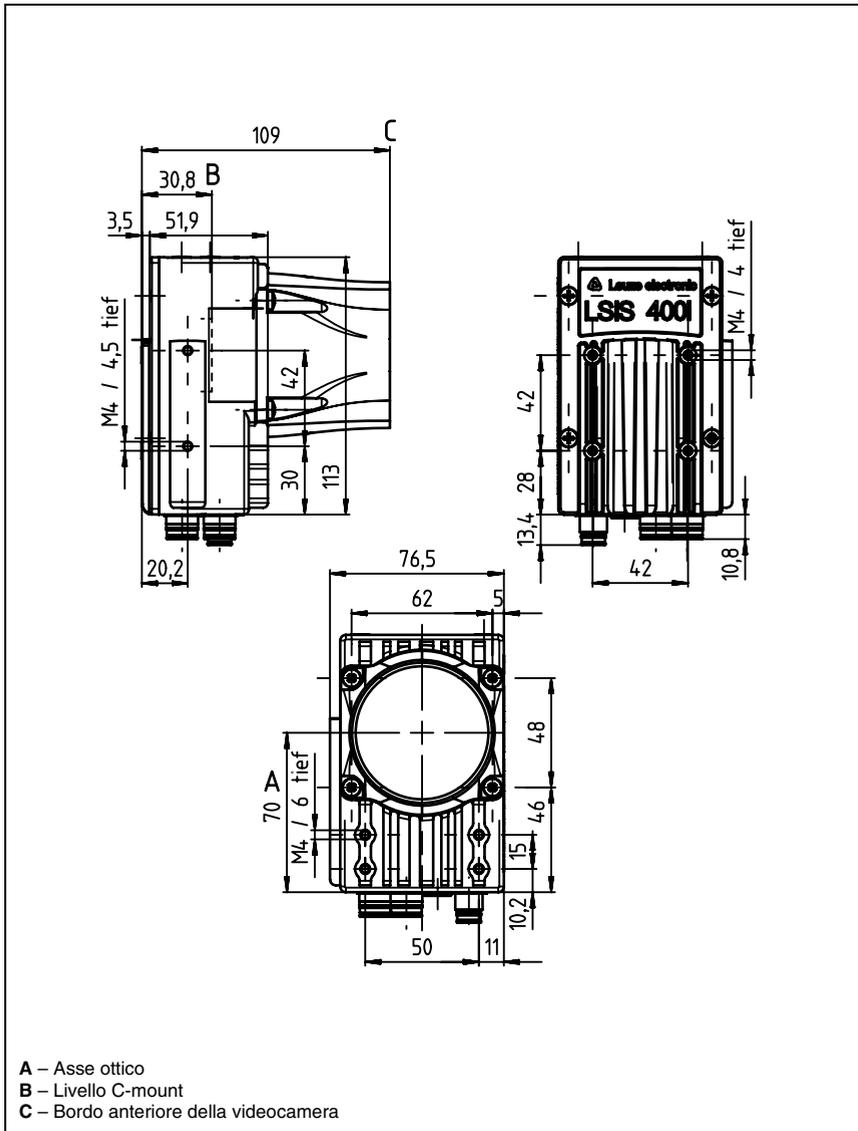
Disegno quotato smart camera LSIS 4xx*i* - Apparecchi per obiettivi con C-mount
